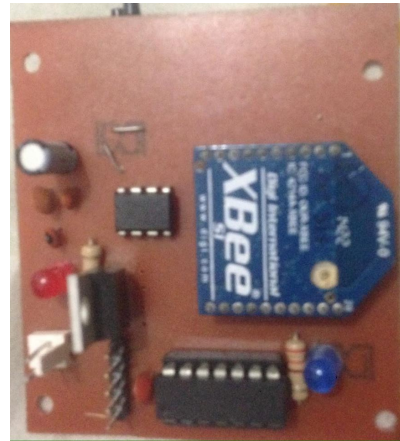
Diseño PCB de circuito: Sensor de presión MP3V5004DP.
